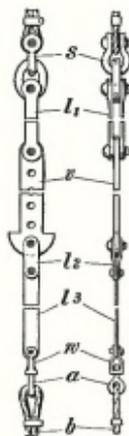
<sup>1)</sup> Unterselgehänge mit Ausgleichvorrichtung für Seillängen.
